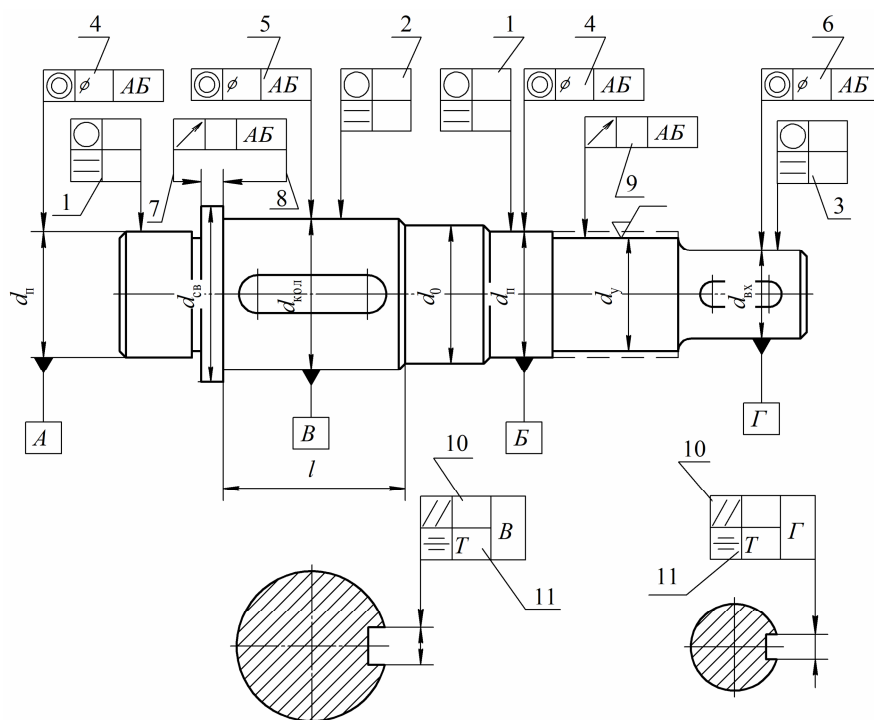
Пример нанесения размеров и условных обозначений
